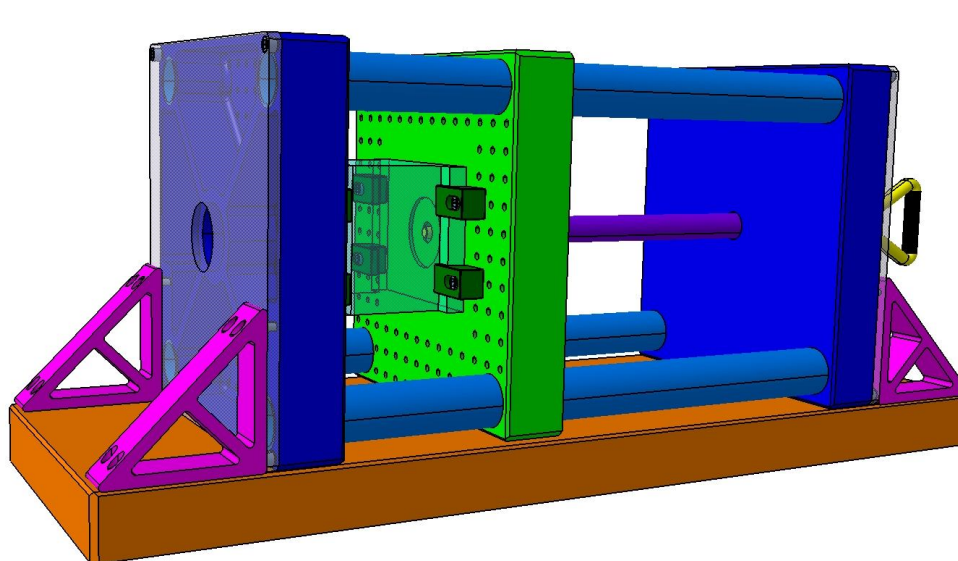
Pohled na zadní stranu duralového pneumatického mechanismu
